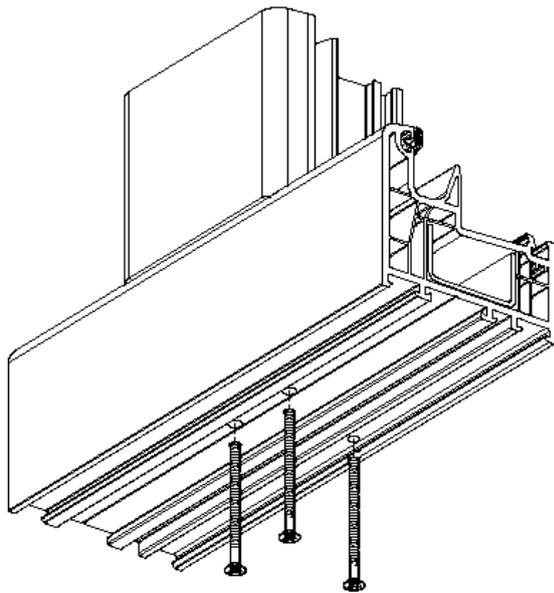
Assemblage mécanique en T de type Assemblage par vis
